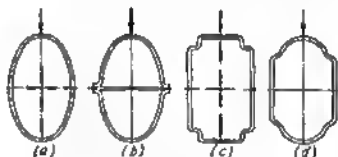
Secciones de vigas de paredes delgadas de elevada rigidez
